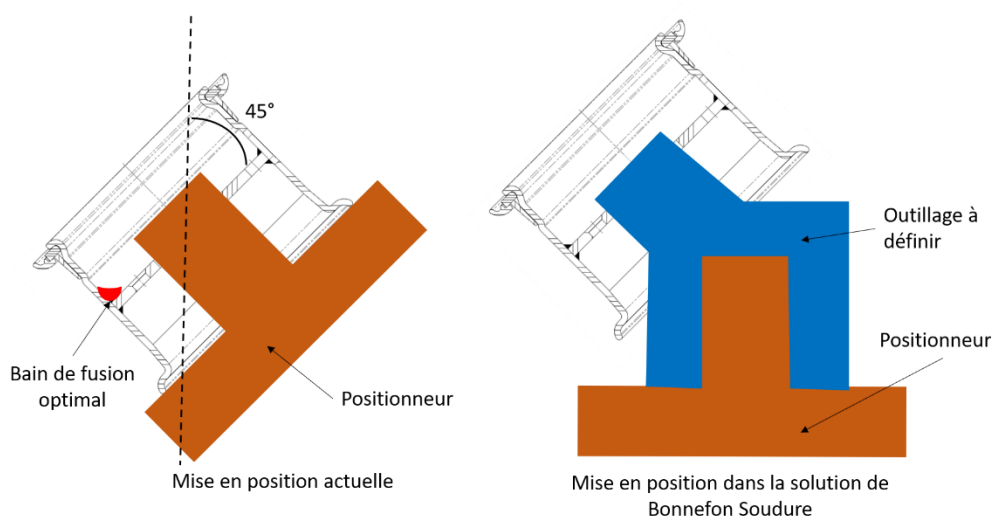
Schéma du montage préconisé pour la solution de Bonnefon Soudure
